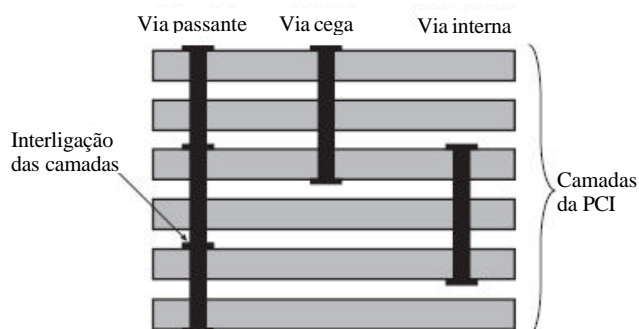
Corte de uma placa de circuito impresso de múltiplas camadas.
